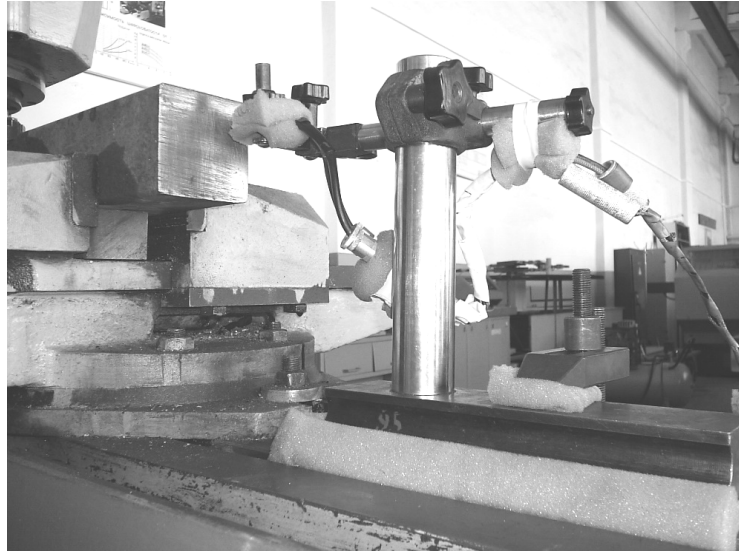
Вимірювальний стенд на фрезерному верстаті ЛГ 26:
